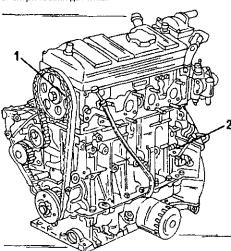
Установка штифтов для блокирования положения газораспределительного механизма.
